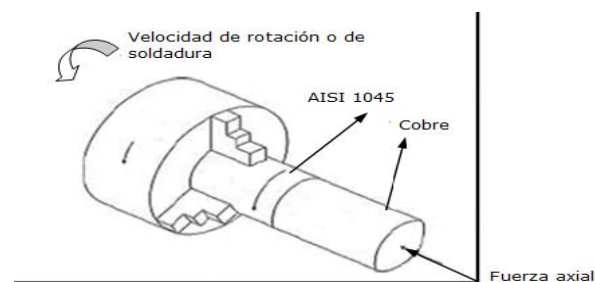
Procedimiento empleado para la soldadura por fricción radial o rotativa.
